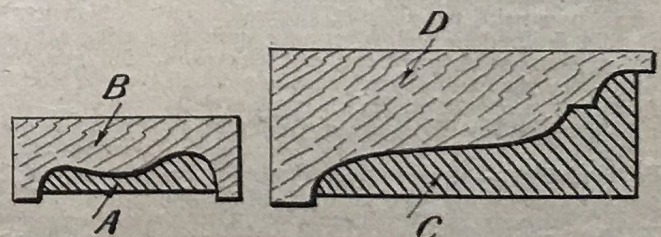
PLACAGE DES MOULURES: A, moulure à plaquer; B, calle (cadres); C, corniche de meuble à plaquer; D, calle.
